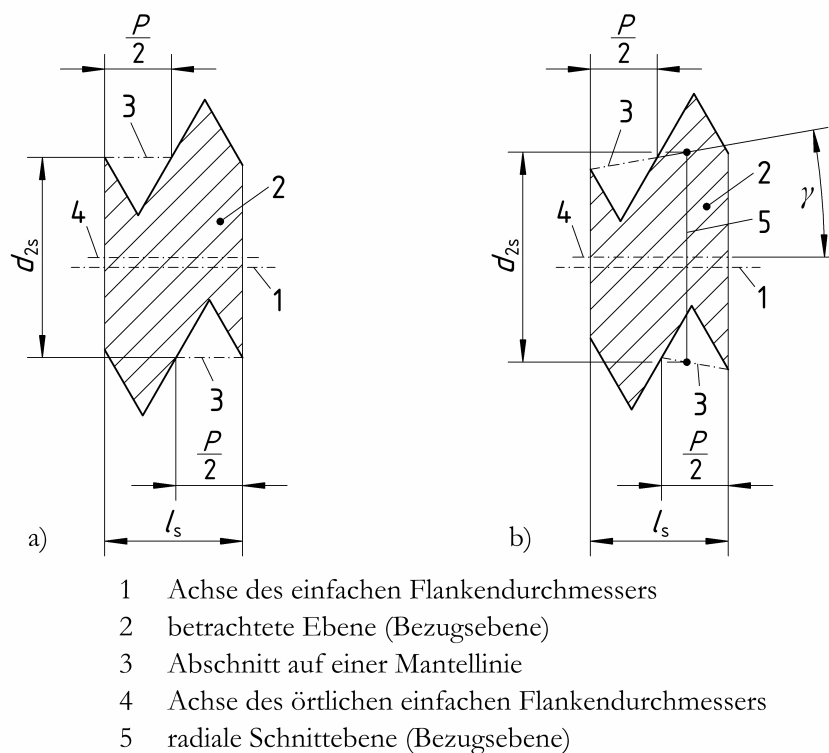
einfacher Flankendurchmesser a) eines zylindrischen und b) eines kegeligen eingängigen Außengewindes
